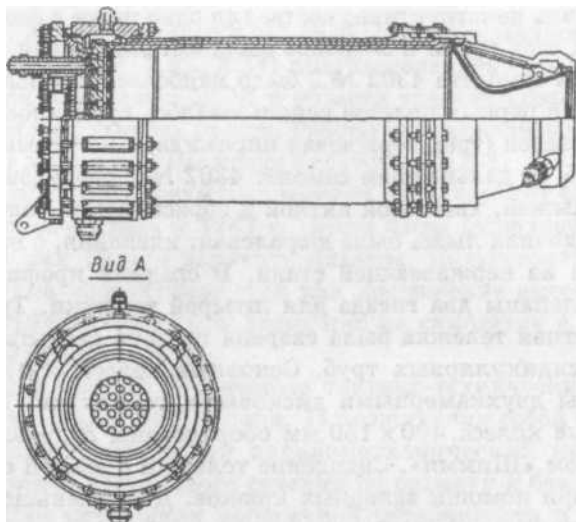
Жидкостный ракетный двигатель РД-1М
